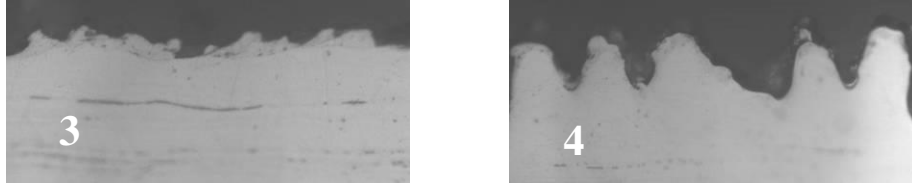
Macrographies des fonds d'usinage, classement des états de surface :
